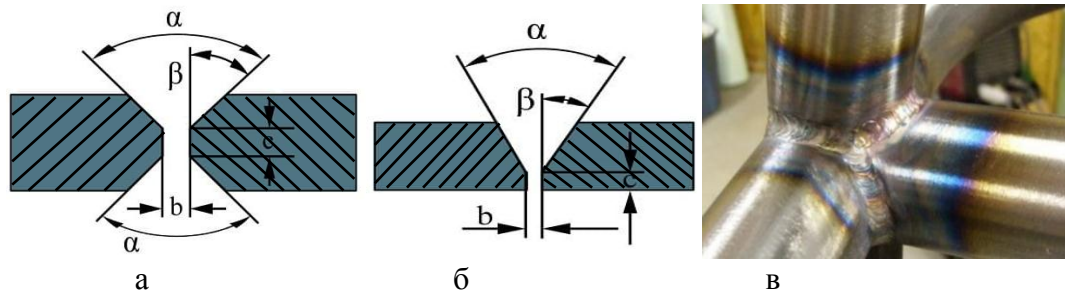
Схеми розділок під зварювання з обробленими перлітними крайками:
